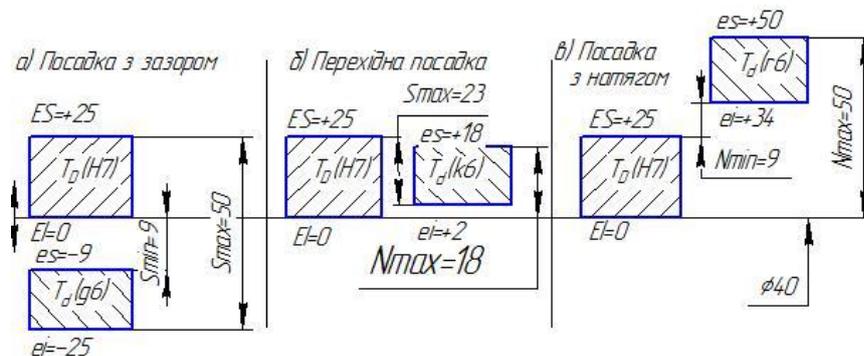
Схема розташування полів допусків посадок
